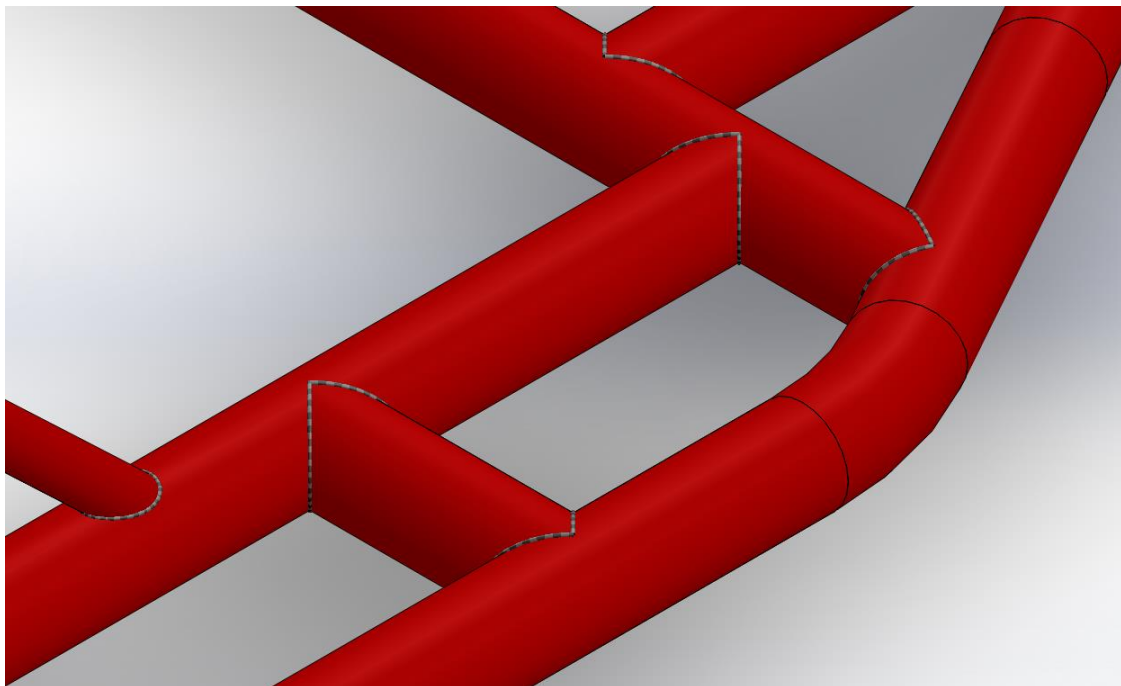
detalle cordones de soldadura. Fuente: propia.
